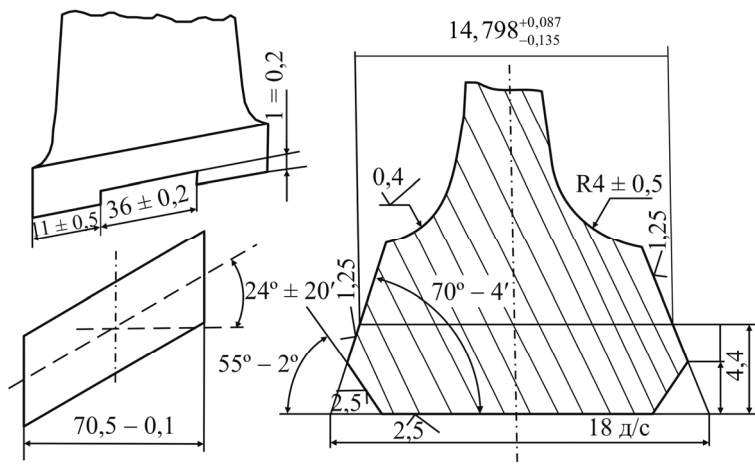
Эскиз замка лопатки компрессора двигателя ПС90 2А из титанового сплава ВТ8, обрабатываемого протягиванием
